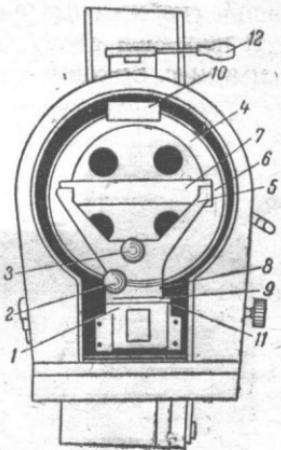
Вид сзади на зеркальную лампу в фонаре: 1—винт крепления основания кронштейна зеркала; 2—рукоятка бокового перемещения; 3—рукоятка вертикального наклона зеркала; 4—оправа зеркала; 5—кронштейн вертикального наклона; 6—винты; 7—дужка с ушками; 8—основание; 9—кронштейн; 10—заслонка; 11—винт, 12—рукоятка заслонки
